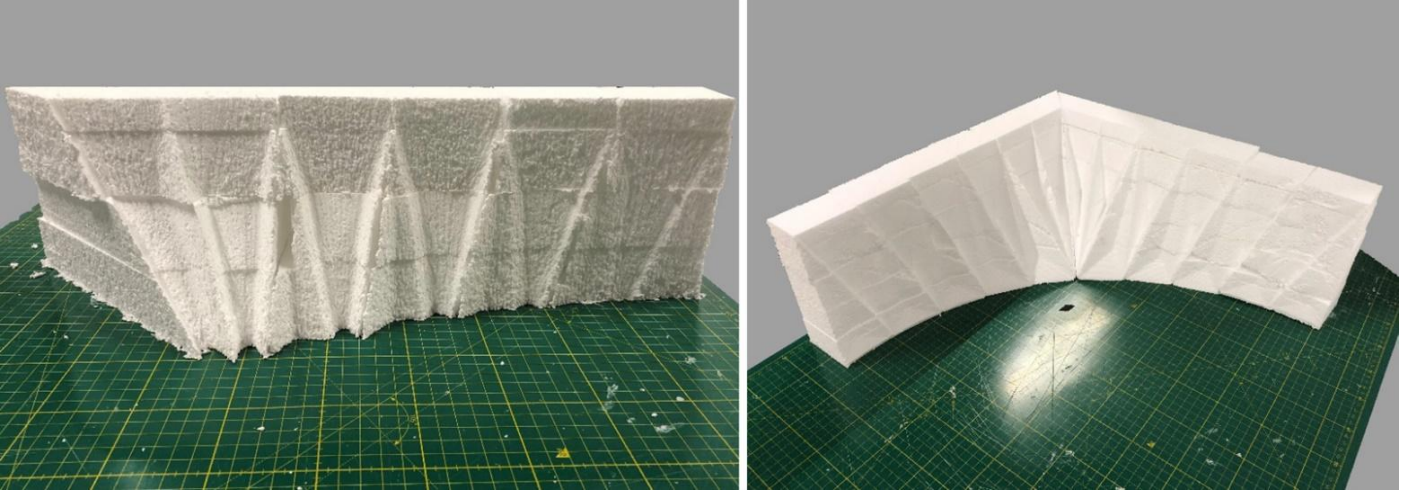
Robot kola entegre edilmiş spindle motor ile gerçekleştirilen frezeleme işlemleri
